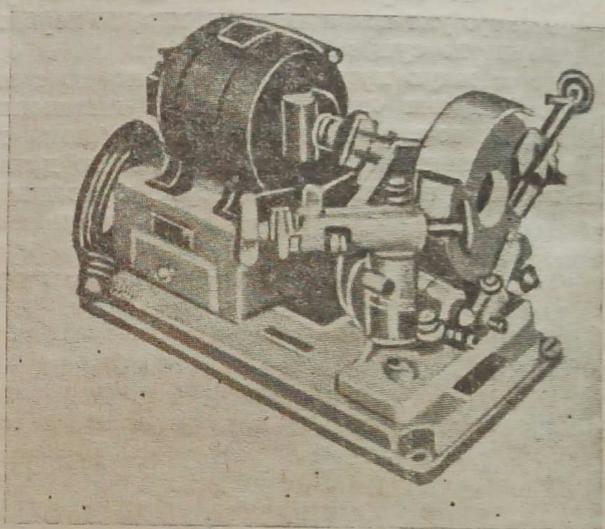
Настольный станок для шлифовки клапанов с приводом от электромотора
